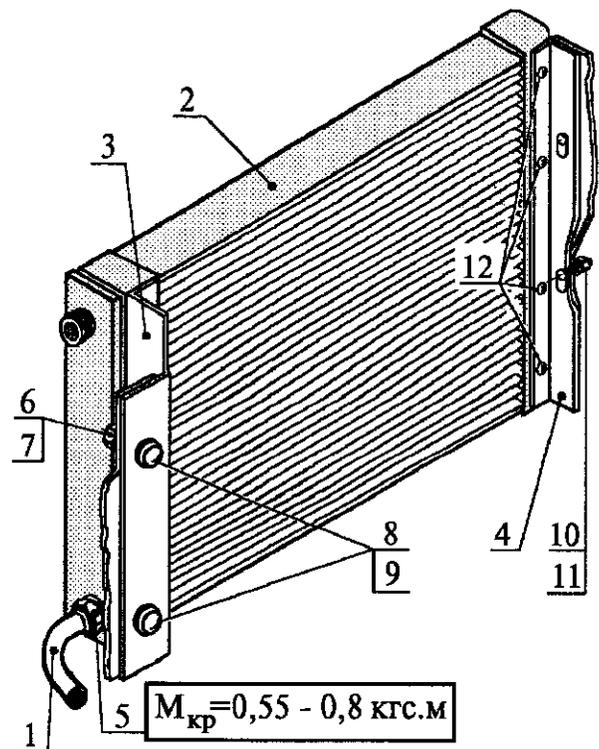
Установка конденсатора с отводящей трубкой в сборе на автомобиль ГАЗ-3110:
